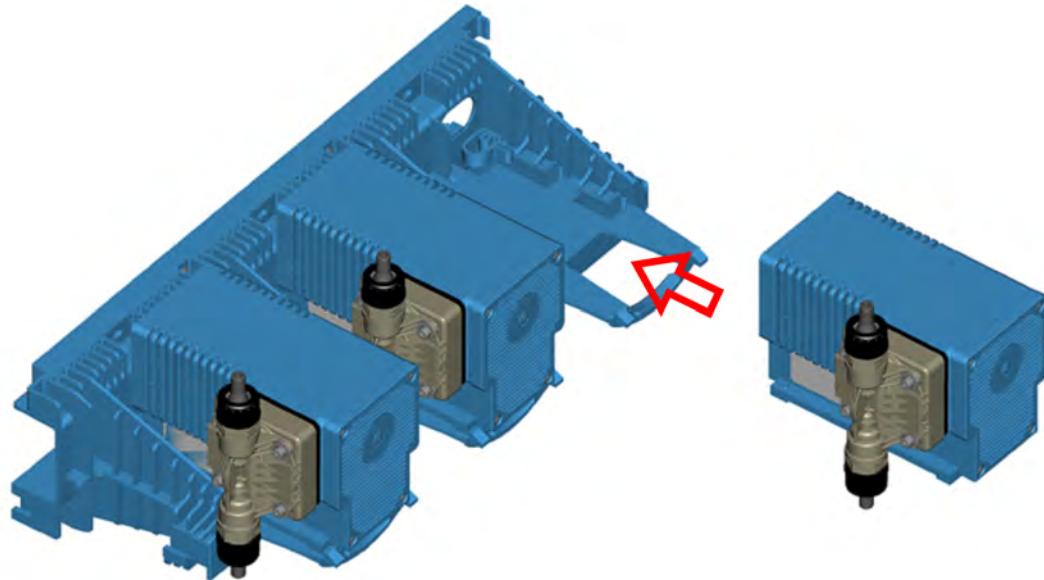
Beispiel: 3 Konsolen mit Pumpen bestückt
